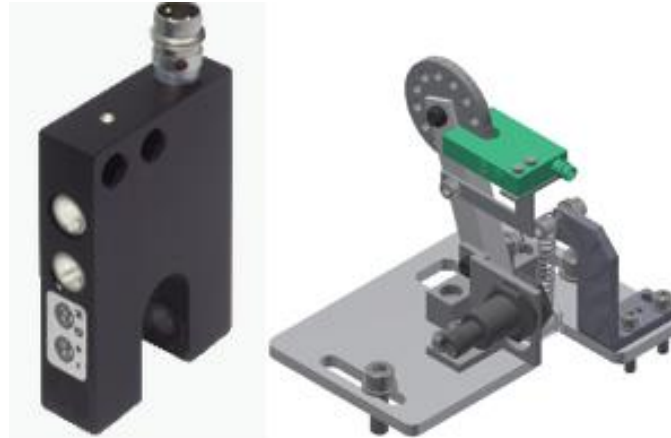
Sensor óptico de horquilla y herradura. Ensamble en el conjunto
